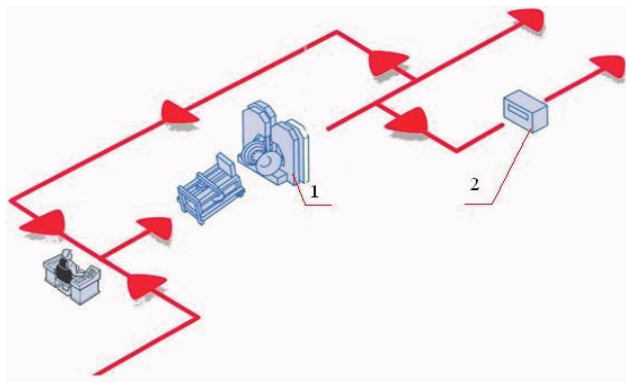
Компоновка фрезернопильной линии: 1 - фрезерно-ленточнопильный агрегат (ФЛПА); 2 - обрезной станок.
